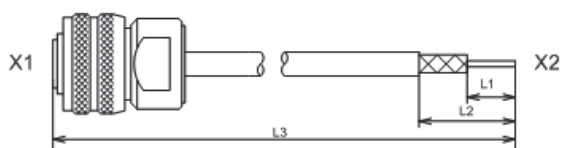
Заготовка кабельной сборки, оснащённая кабельным соединителем с одной стороны
